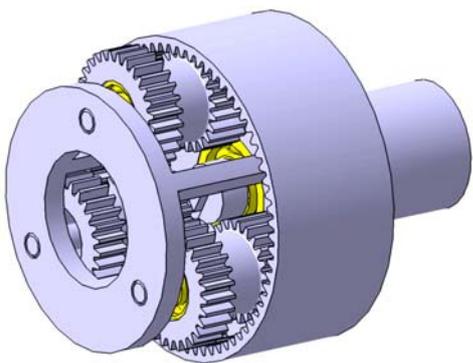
Планетарный редуктор, выполненный по схеме 3К
